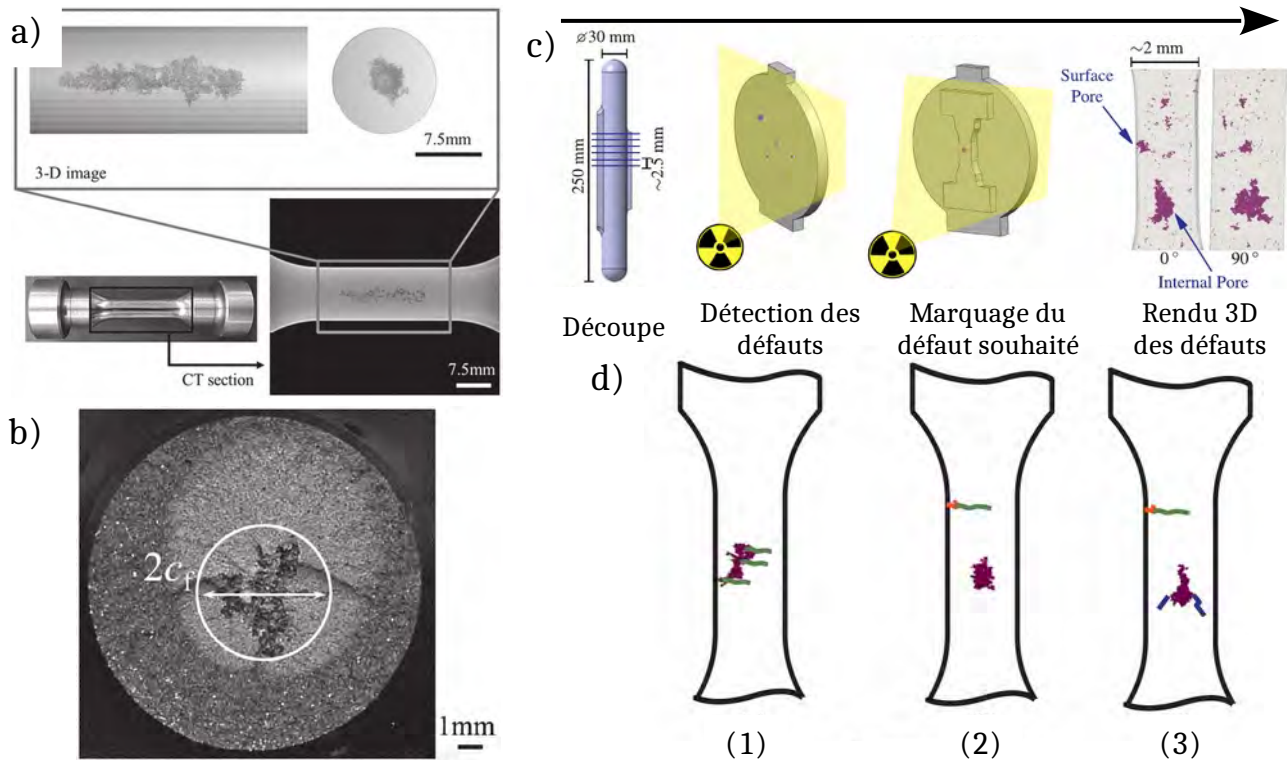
Fabrication d'éprouvettes de fatigue à défaut interne contrôlé par fonderie. a) Inspection par tomographie RX d'une éprouvette (barreau) de fonte GS [IKE 17] présentant un défaut interne ayant mené à la rupture en fatigue. b) Faciès de rupture correspondant. c) Processus de détection et de choix de la retassure interne dans un alliage d'aluminium A357-T6 [SER 18]. d) Illustration schématique de la compétition entre défauts de surface et défauts en volume pour l'amorçage de fissure de fatigue.
